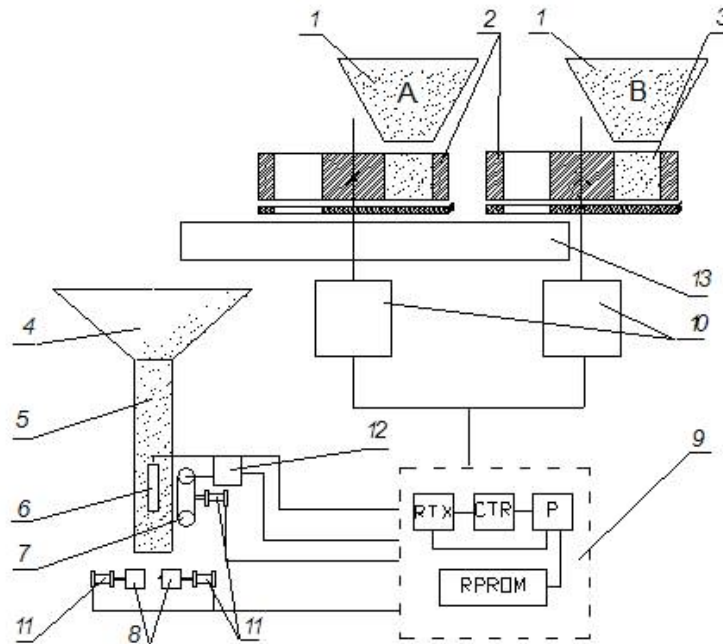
Схема компонування машини для багатоконпонентного дозування сипких речовин: 1– бункери; 2 – дозатори; 3 – лоток; 4 – приймальний бункер; 5 – формувальна труба; 6 – губка зварювання поздовжнього шва пакета; 7 – механізм протягування рукава; 8 – губки зварювання поперечних швів пакета; 9 – блок керування; 10 – приводи вивантажування сипких компонент; 11 – пневмоциліндри; 12 – приводи переміщення рукава; 13 – лоток
